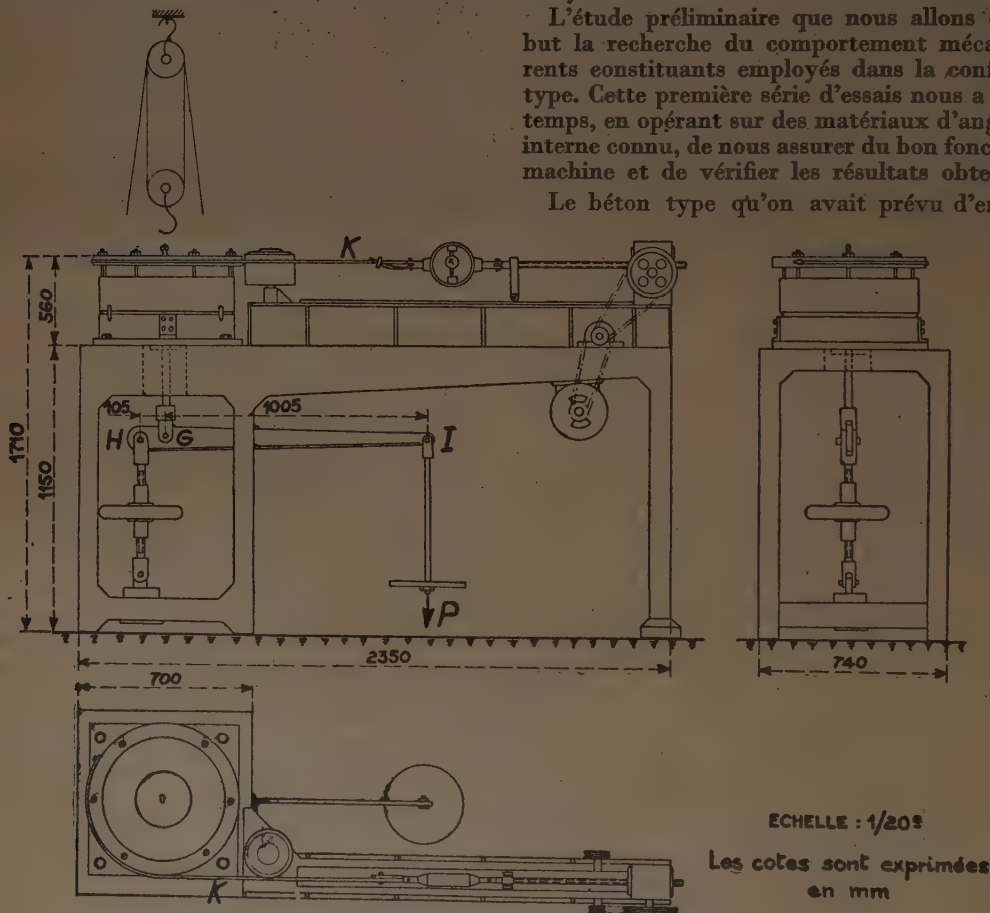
Vue d'ensemble de la machine de cisaillement.
